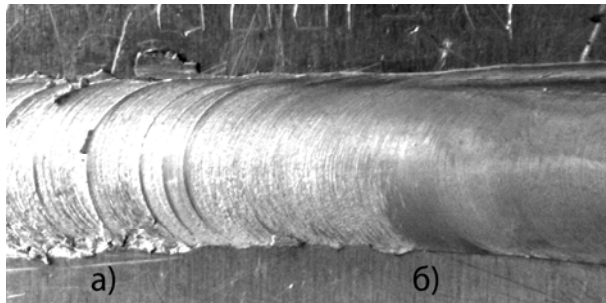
Вигляд поверхні зварного з'єднання зі сторони поверхні переміщення робочого інструмента: а – ділянка з підвищеною шорсткістю зони термічного впливу; б – ділянка шву з високою якістю
